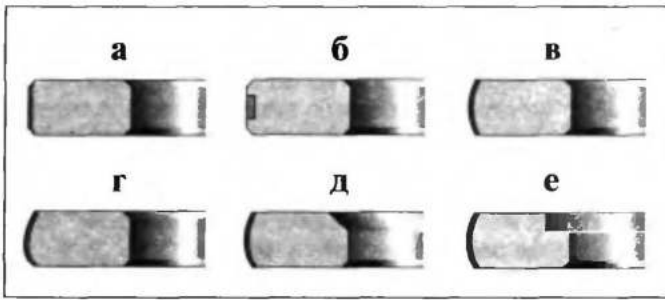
Профили верхних компрессионных колец двигателей легковых автомобилей:
